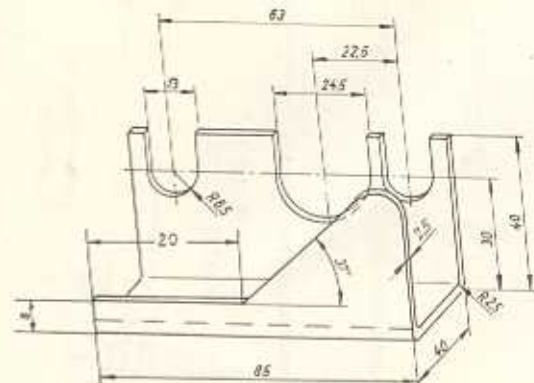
Einstelllehre für Ritzellausch (Maßskizze)
